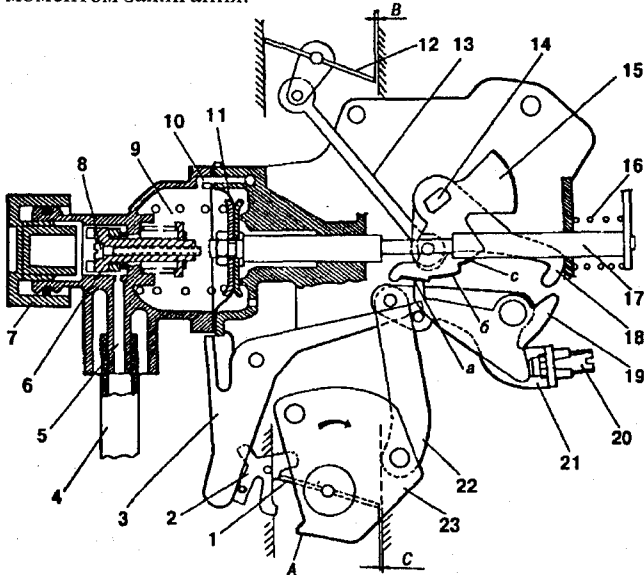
Схема полуавтоматического пускового устройства карбюратора: 1 – дроссельная заслонка первой камеры; 2 – рычаг блокировки второй камеры; 3 – рычаг привода блокировки; 4 – шланг к ресиверу; 5 – штуцер; 6 – плунжер; 7 – упор регулировки второй ступени; 8 – регулировочный винт; 9 – диафрагменная полость; 10 – воздушный канал из задрозельного пространства карбюратора; 11 – диафрагма пускового устройства; 12 – воздушная заслонка; 13 – тяга привода воздушной заслонки; 14 – ось пускового устройства; 15 – кулачок; 16 – пружина штока; 17 – шток диафрагмы пускового устройства; 18 – крючок блокировки второй камеры; 19 – рычаг привода; 20 – регулировочный винт приоткрывания дроссельной заслонки первой камеры; 21 – рычаг приоткрывания дроссельной заслонки; 22 – тяга приоткрывания дроссельной заслонки; 23 – рычаг управления дроссельными заслонками; А – упор блокировки второй камеры; В – пусковой зазор у воздушной заслонки; С – пусковой зазор у дроссельной заслонки. а, б, с – первая, вторая и третья ступени кулачка
